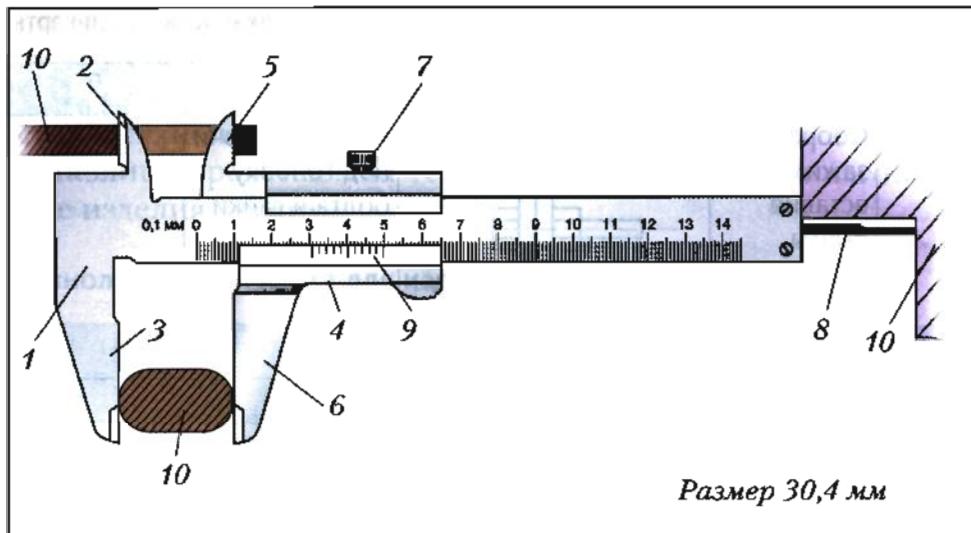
Устройство штангенциркуля: 1 – штанга; 2 – неподвижная верхняя измерительная губка; 3 – неподвижная нижняя измерительная губка; 4 – рамка; 5 – верхняя подвижная измерительная губка; 6 – нижняя подвижная измерительная губка; 7 – зажимный винт; 8 – глубиномер; 9 – ноуиус; 10 – измеряемые детали
